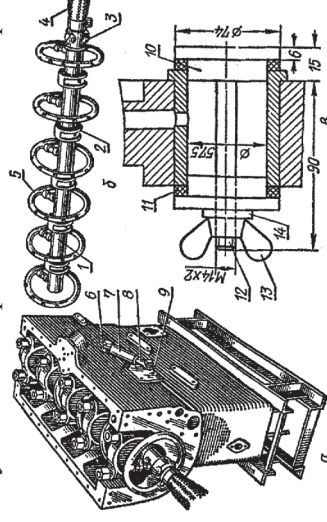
Приспособление для промывки масляных каналов и внутренних поверхностей блока двигателя:
